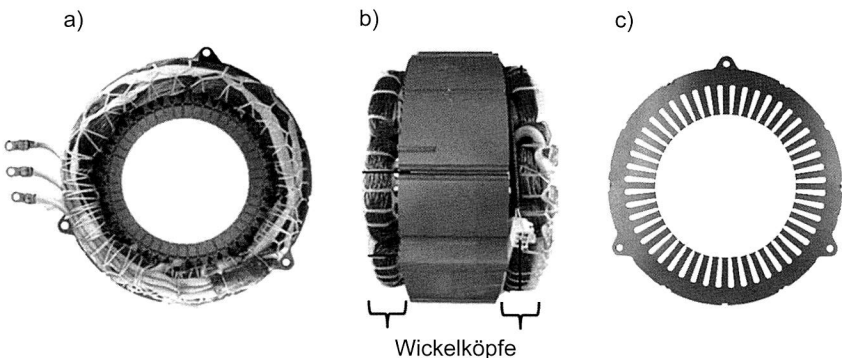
Beispiel Elektromotor in Vollschnitt-Ausführung (Toyota Prius); a) Stator Frontansicht, b) Stator Seitenansicht, c) Stator Blechschnitt [34]
